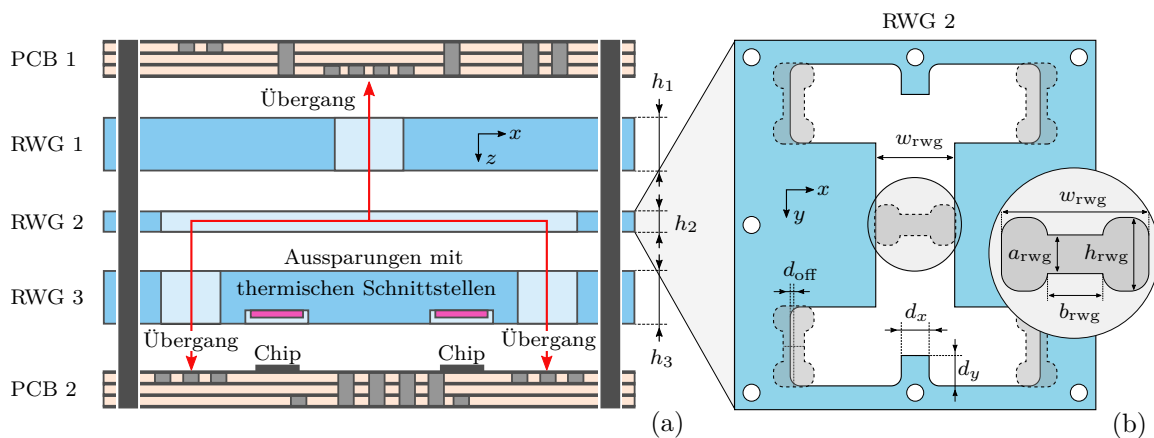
(a) Querschnitt der gestapelten Anordnung von PCB 1 (Treiber-PCB), PCB 2 (Frontend-PCB) und den drei Aluminiumplatten RWG 1–RWG 3 und (b) Draufsicht von RWG 2. Der Stapelaufbau von RWG 1–RWG 3 bildet einen reaktiven Leisterteiler und -kombinierer in Hohlleitertechnologie.
